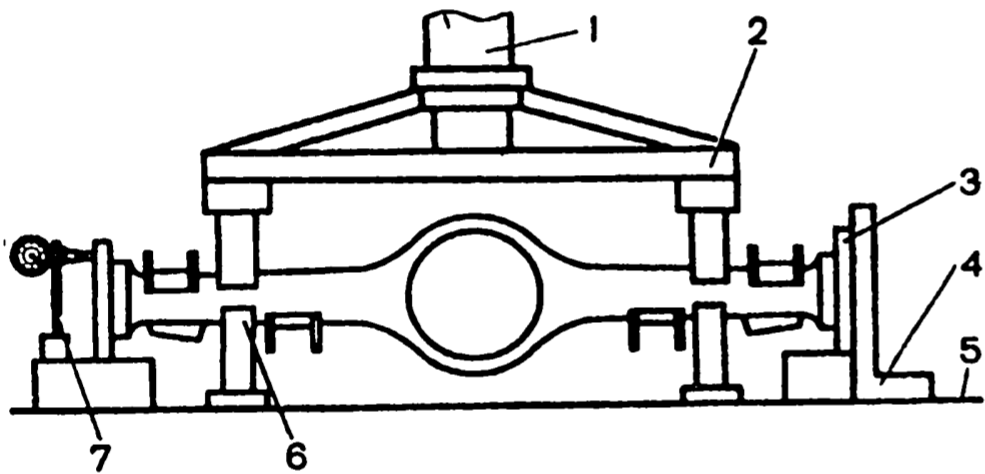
Схема правки балки заднего моста: 1 - гидроцилиндр; 2 - прижимная траверса; 3 - фланец А.70172; 4 - угольник; 5 - стол пресса; 6 - упор; 7 - стойка индикатора
